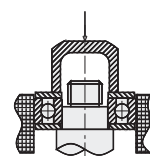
Одновременная запрессовка внутреннего и наружного колец
